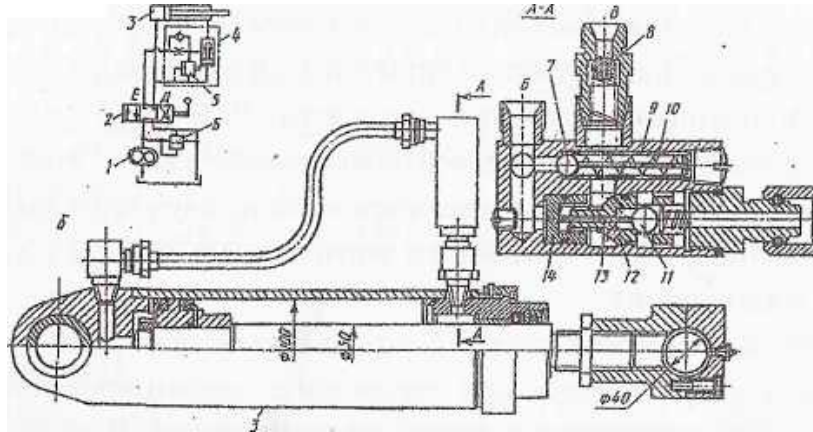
Принципова схема гідроприводу вантажопідйомного борту (а) і конструкція гідроциліндра (б) з гідрозамком: 1 — шестерінчастий насос; 2 — золотниковий розподільник; 3 — гідроциліндр; 4 — гідрозамок; 5,6 — запобіжний клапан; 7 — кулька; 8 — дросель; 9 — хрестовина; 10 — пружина; 11 — кулька; 12 — сідло; 13 — голка; 14 — поршень гідрозамку; б, В, Г-порожнина; Д, Е-канал.
